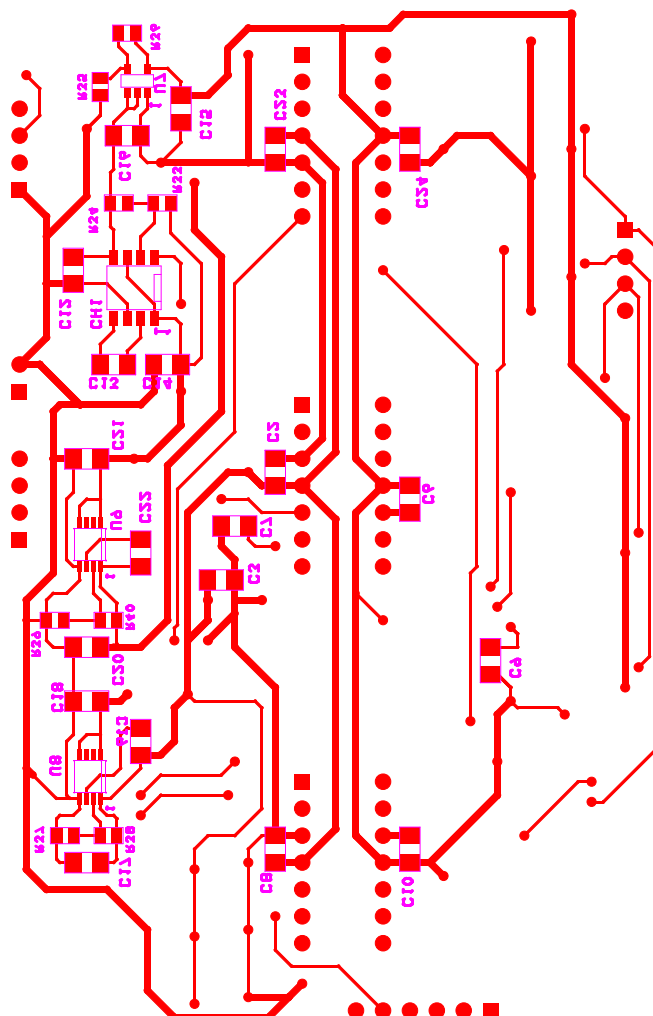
Vista inferior del PCB de la etapa de I/O de MECEHA.
